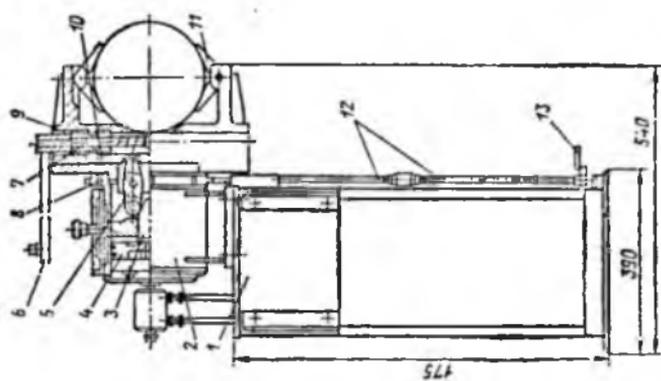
Стенд-контроваль для сборки мелких сборочных единиц:
